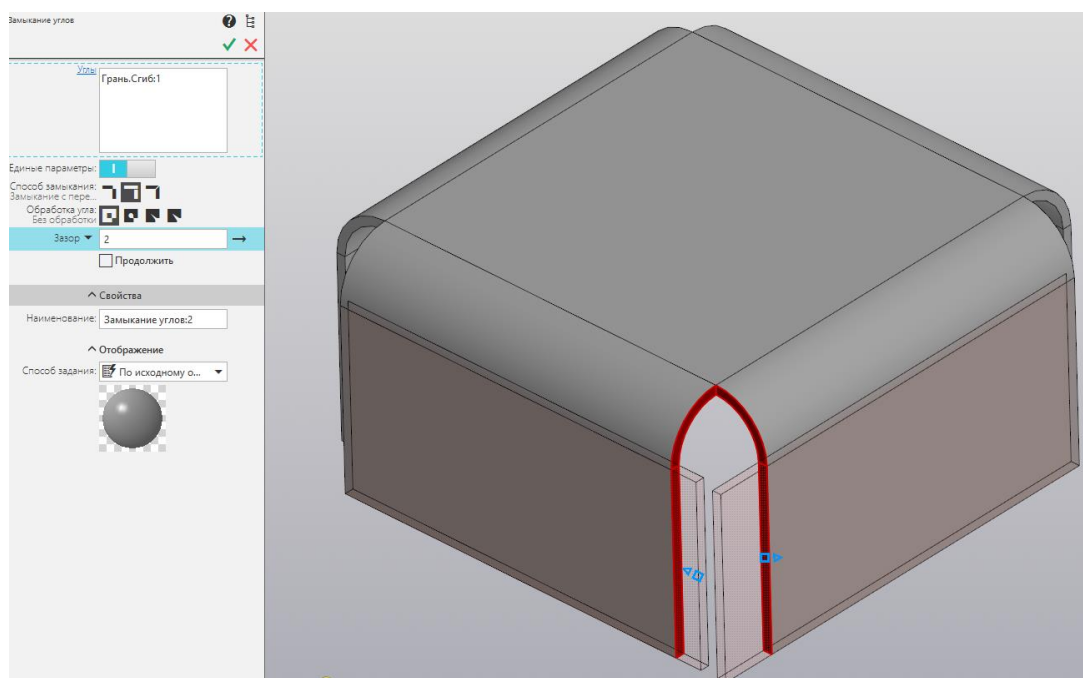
Замыкание угла с перекрытием с зазором
